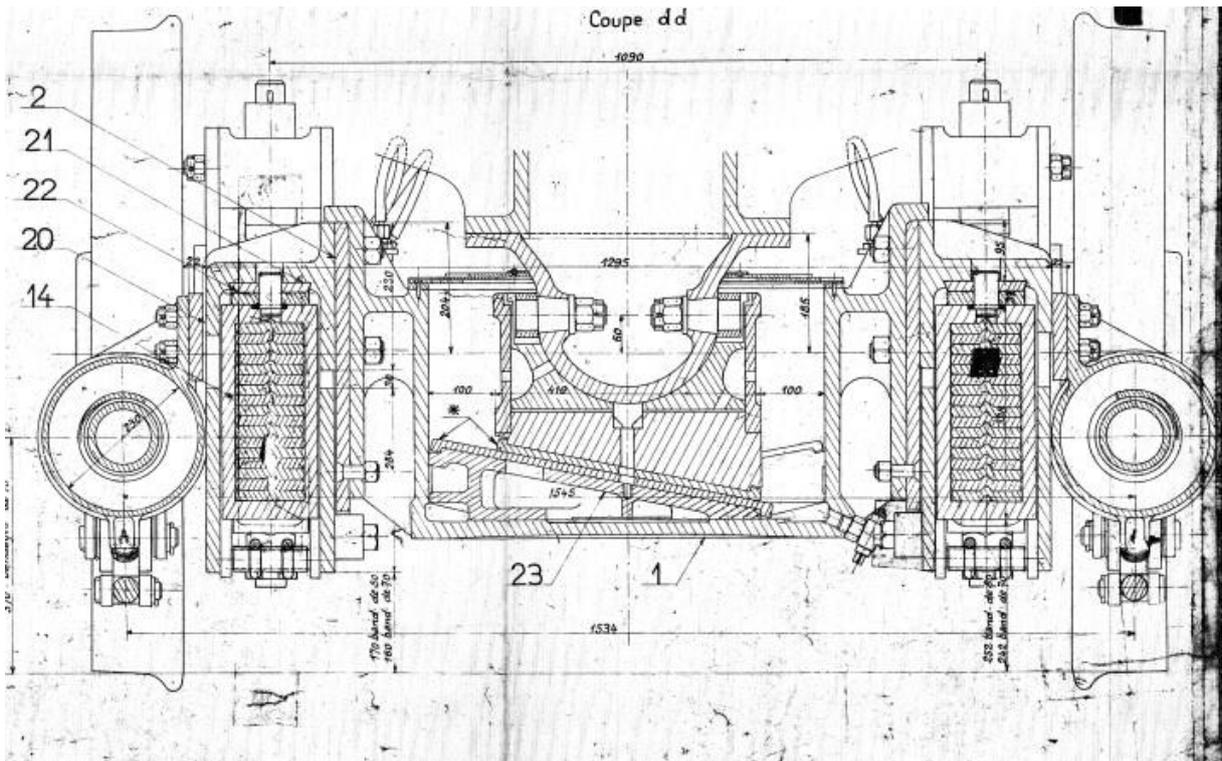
Coupe transversale du bogie 241 P - Plan Schneider.
